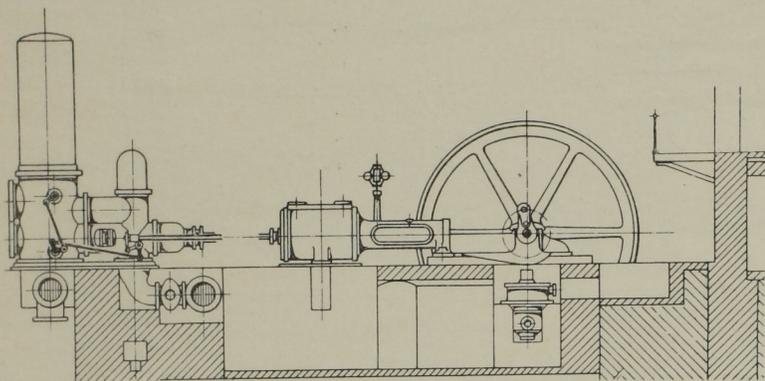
Seitenansicht der Pumpmaschine. Masst. 1:105.
